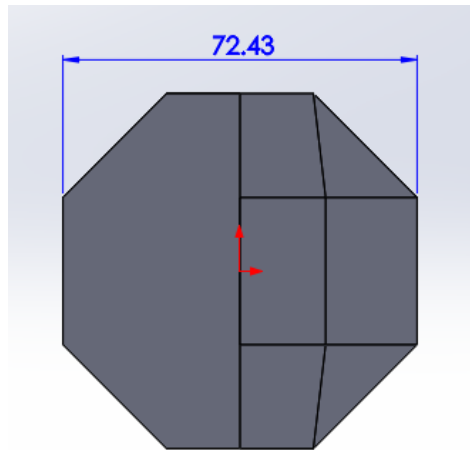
Vista Superior do módulo com dimensão em milímetros (0.07243 metros) da base octaédrica
